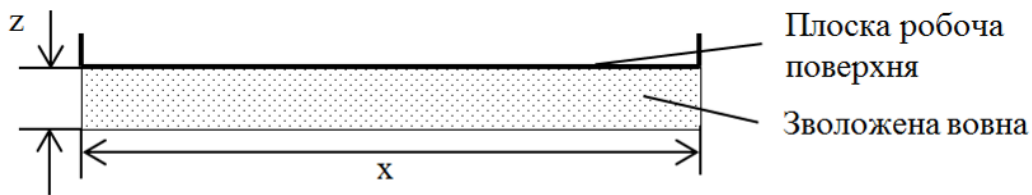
Плоска робоча поверхня верхньої рухомої плити малогабаритної плитно-валяльної машини.
